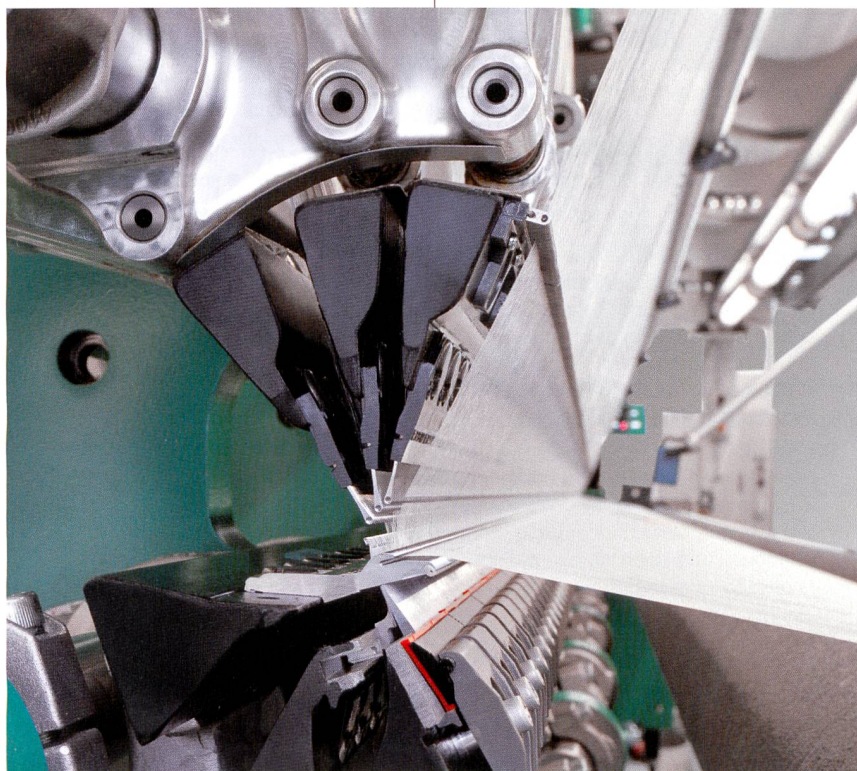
Die Wirkwerkzeuge der HKS 3-M
